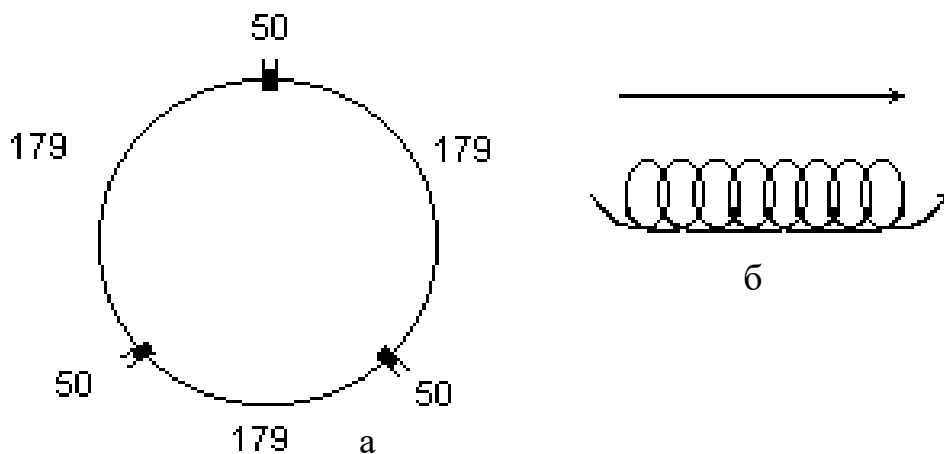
Схема: а – порядку збирання зварного виробу;
